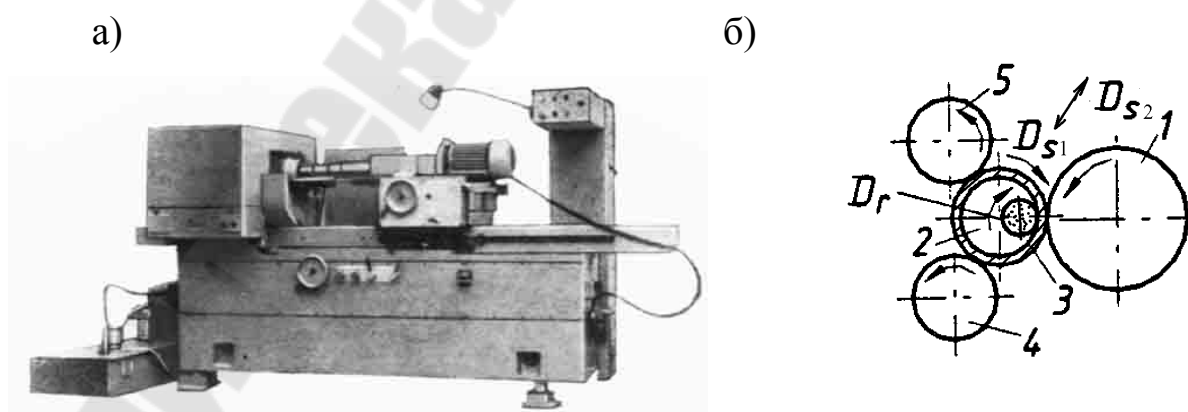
Общий вид бесцентрового внутришлифовального станка (а) и схема бесцентрового шлифования отверстия (б)
